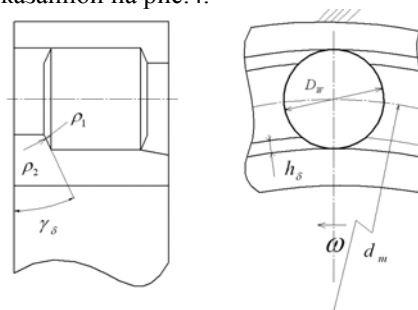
Схема торцевого контакта в цилиндрическом роликоподшипнике
